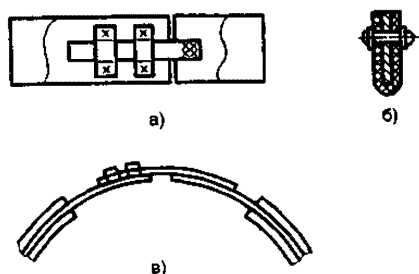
Приспособление (уплотняющее кольцо) для накачки бескамерной шины
